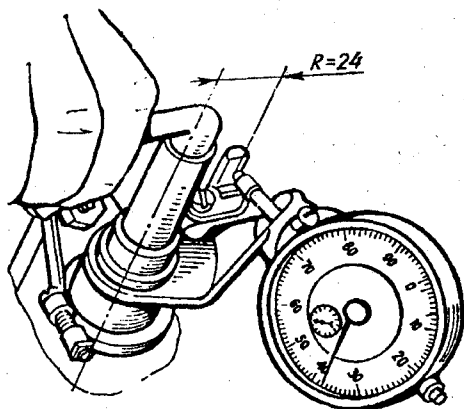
Проверка бокового зазора в зацеплении шестерен привода датчика-распределителя
